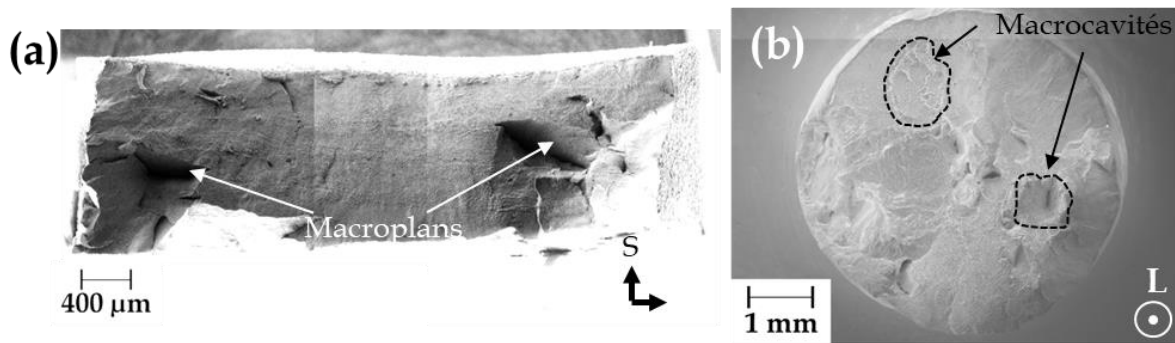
Macrographies du faciès de rupture d'éprouvettes testées en traction uniaxiale :
